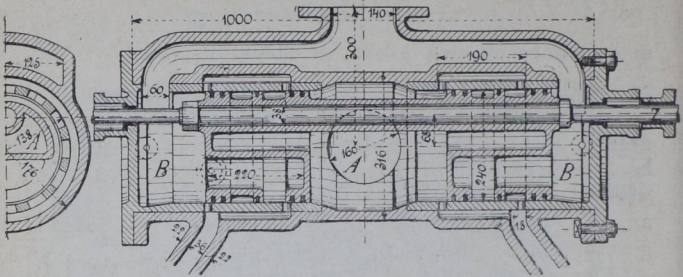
304. Kolbenschieber für 610 Cylinderdurchmesser. 1:15.
